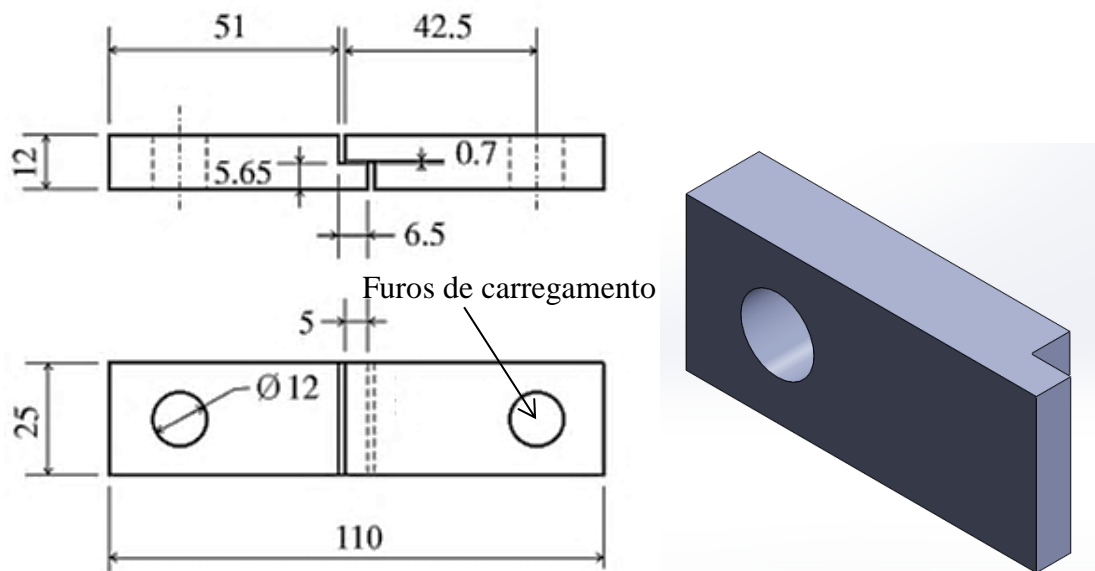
Provette *TAST*, segundo *ISO 11003-2* (dimensões em mm).
